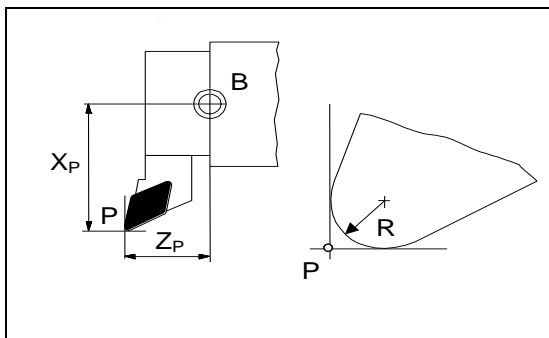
Розташування точки установки інструменту на токарному верстаті з ЧПК
